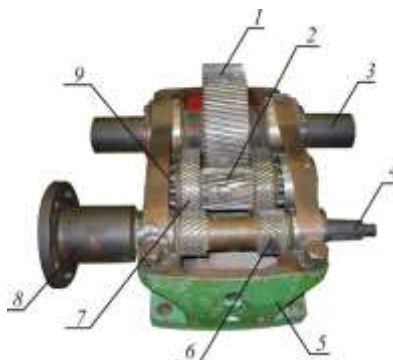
Редуктор двухступенчатый цилиндрический: 1, 7 — зубчатые колеса; 2, 6 — шестерни; 3, 4 — тихоходный и быстроходный валы; 5 — корпус; 8 — полумуфта; 9 — подшипник
